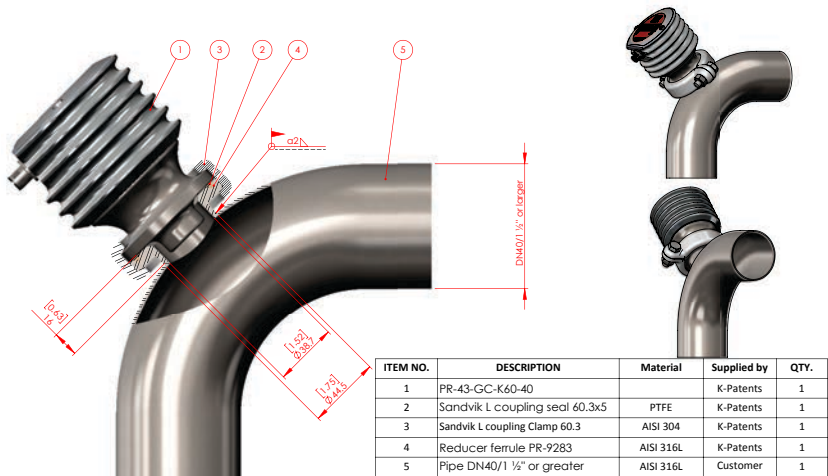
Montaje del PR-43-GC-K60 con férula reductora
